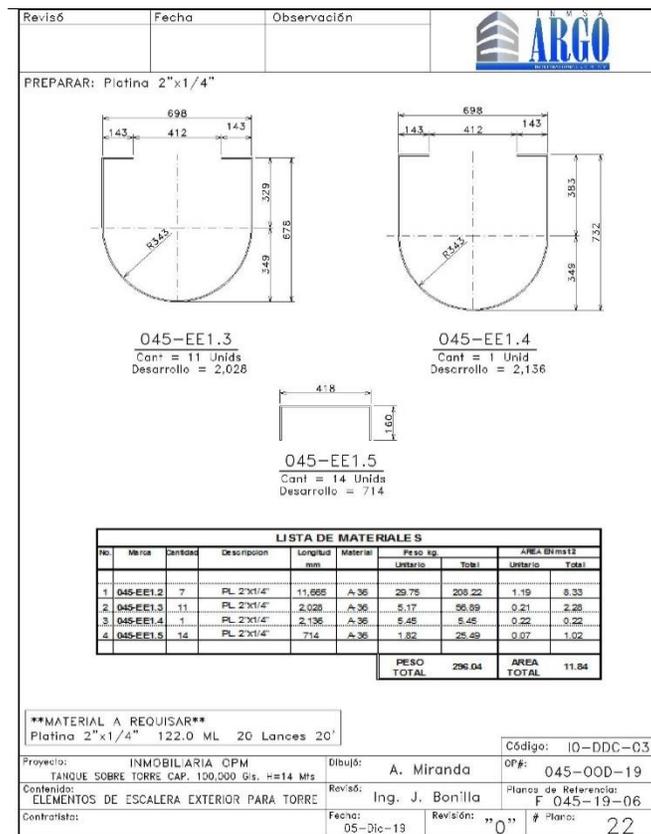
Esquemas de fabricación de elementos de escalera externa
